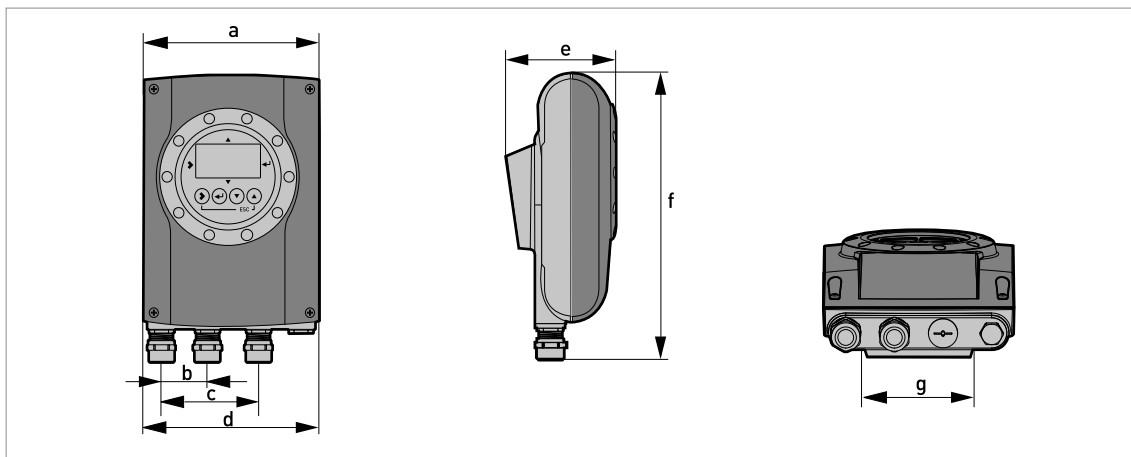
Габаритные размеры устройства компактного исполнения
